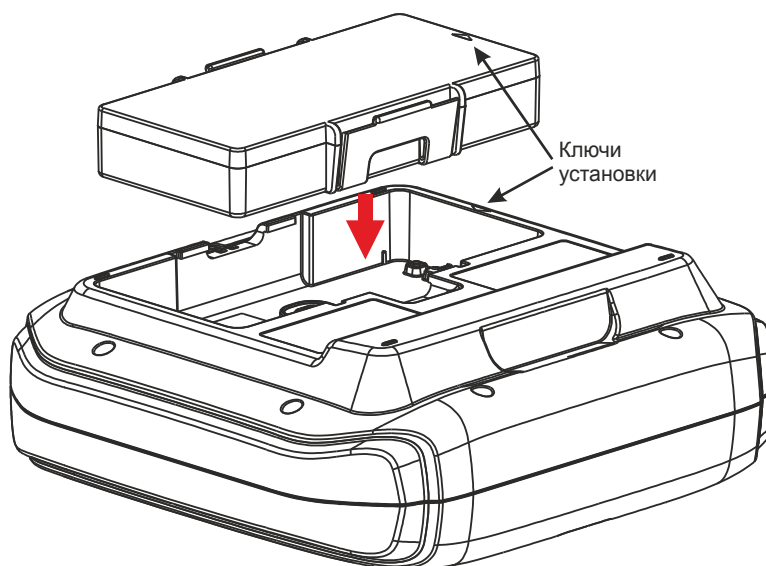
Установка батареи питания в корпус дефибриллятора
